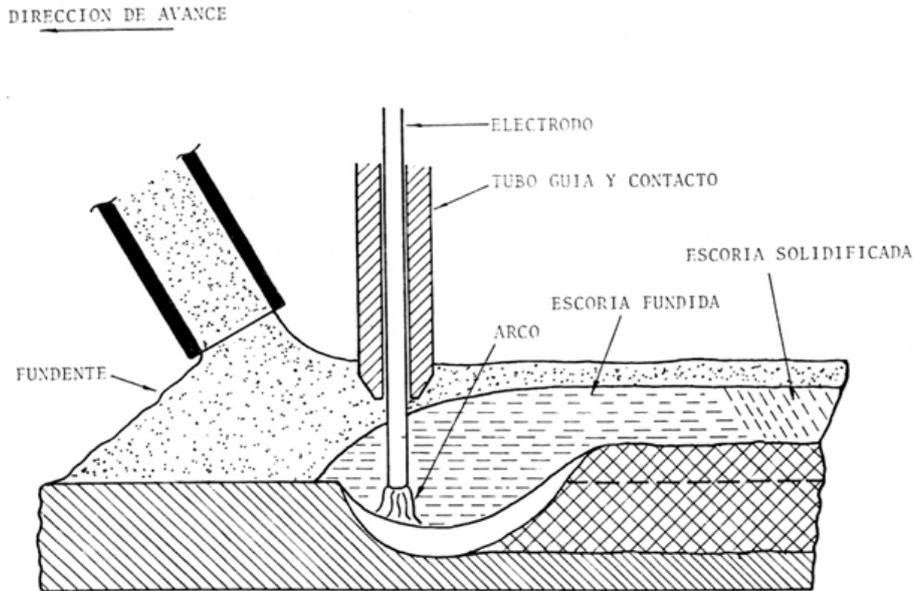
Soldadura por arco sumergido – Fuente: <http://www.histarmar.com.ar/Astilleros/Diccionario/LetraS.htm>
